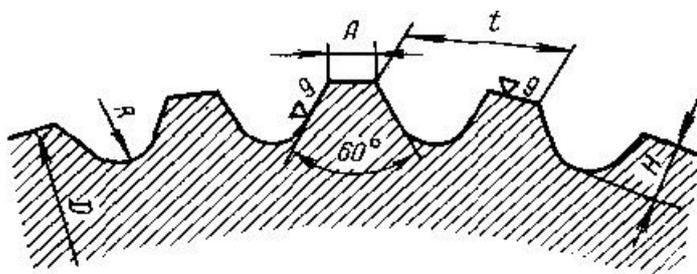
Профиль рифлей цилиндров вытяжного прибора
